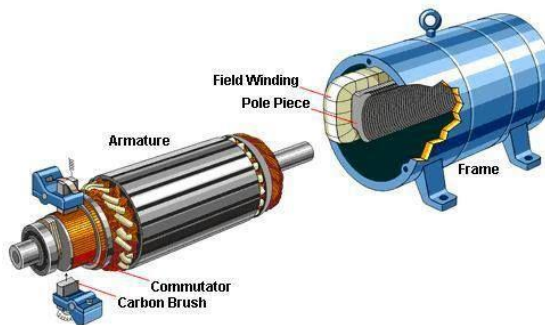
Parts d'un motor (Font: Fitzgerald & Kingsley's Electric Machinery)
